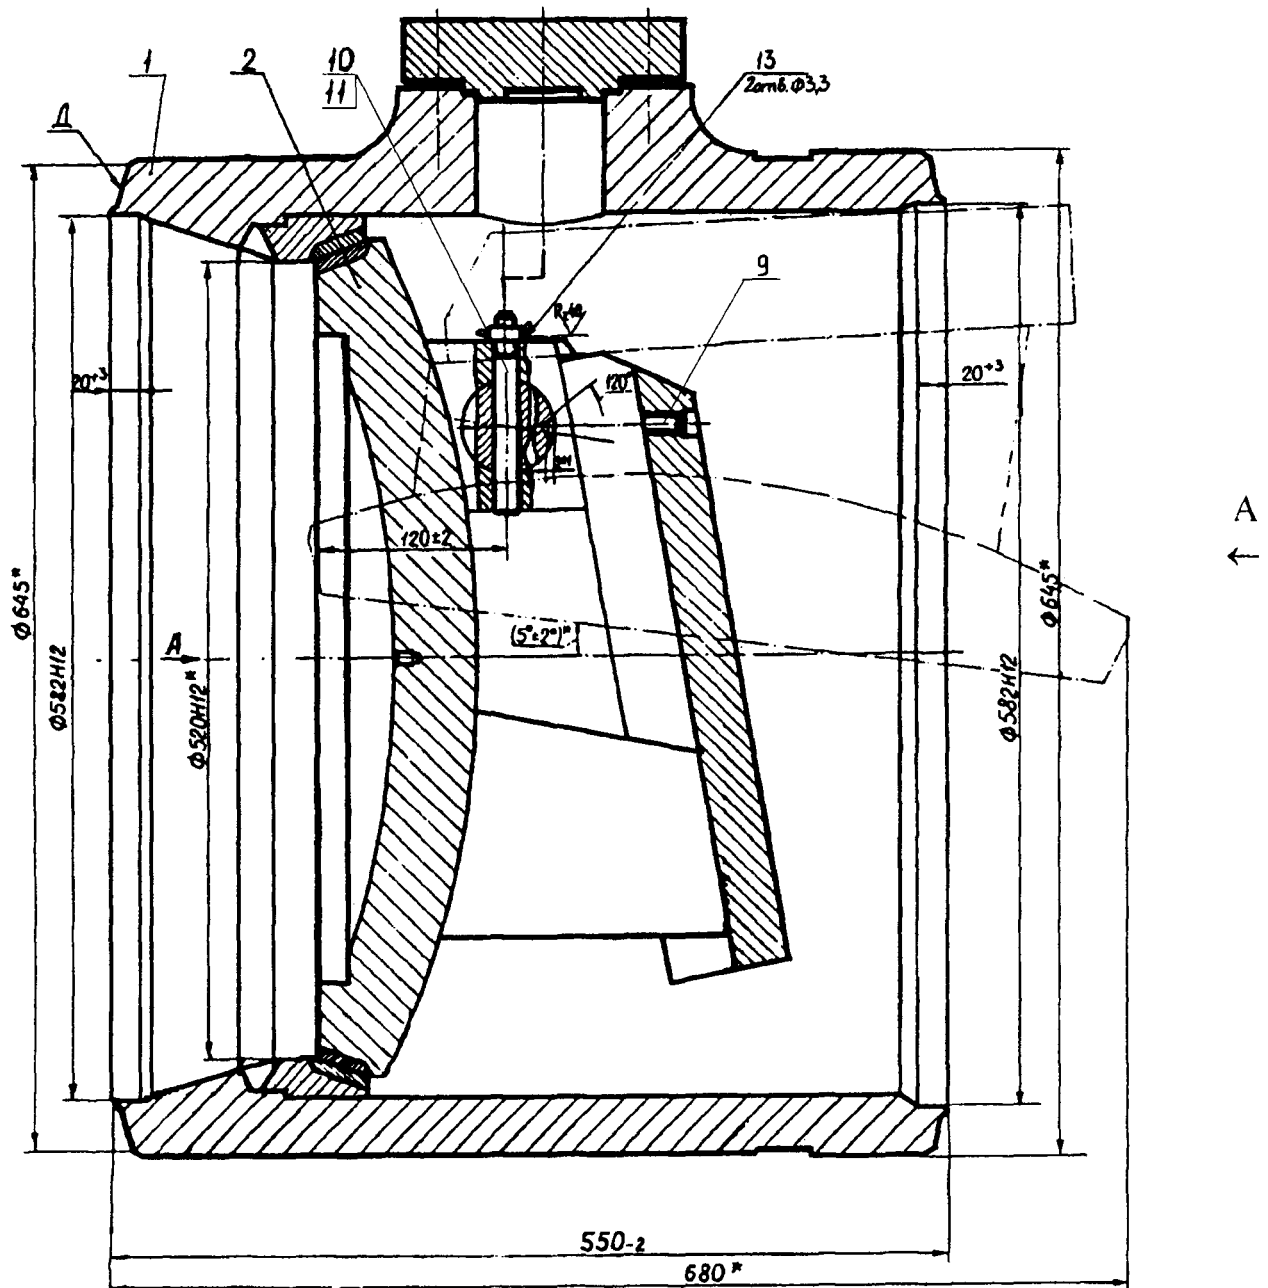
Клапан типа 904-600-0 в сборе
